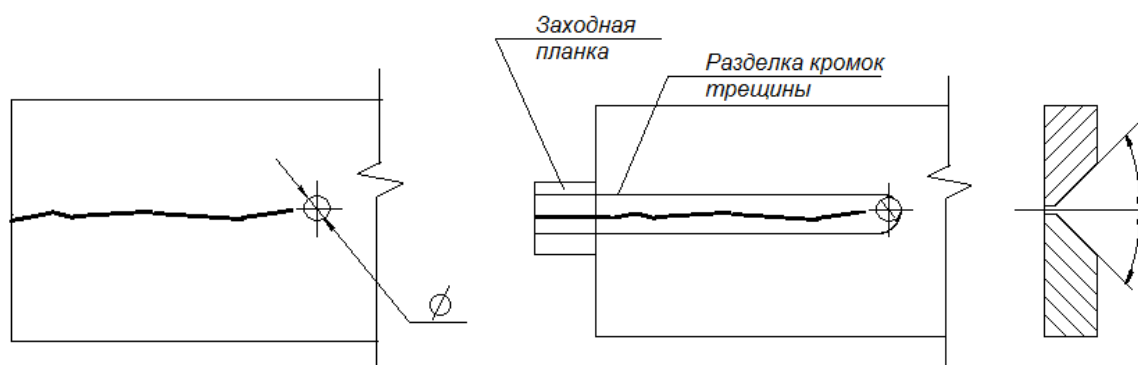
Подготовка трещины к сварке и приварка заходной планки
